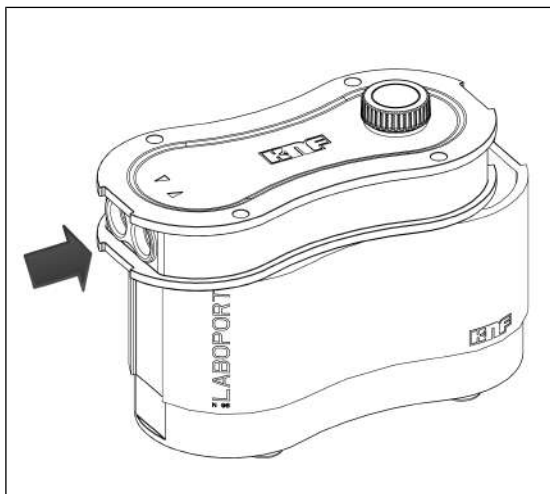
Надвигка крышки корпуса на газовые соединения (закрытие насоса)
